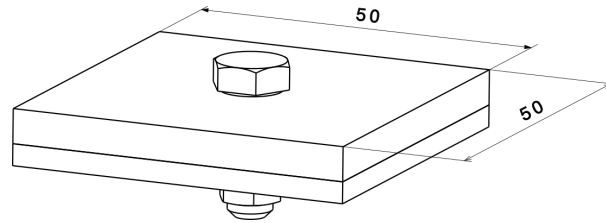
Géométrie de l'assemblage pour l'essai de serrage
